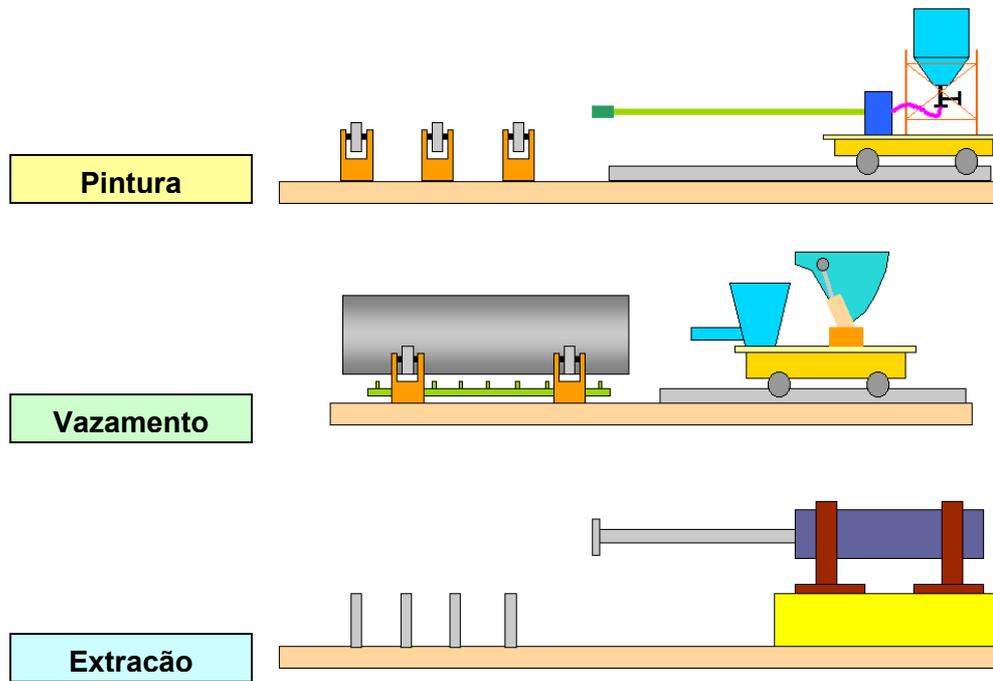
Desenho esquemático de máquina centrífuga de tubos
